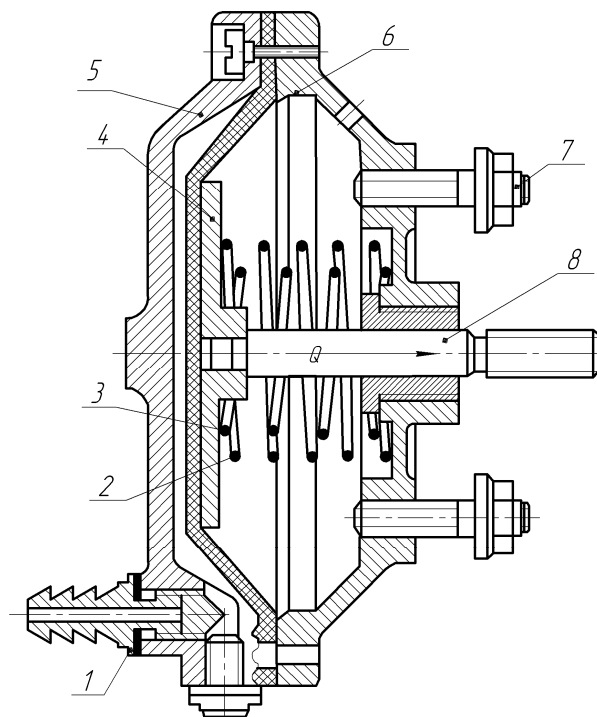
Будова та параметри пневмокамери одnobічної дії: 1 – штуцер; 2, 3 – пружини; 4 – сталевий диск; 5 – корпус; 6 – діафрагма; 7 – шпилька; 8 – шток; Q – зусилля на штоку; d – діаметр сталевого диска
